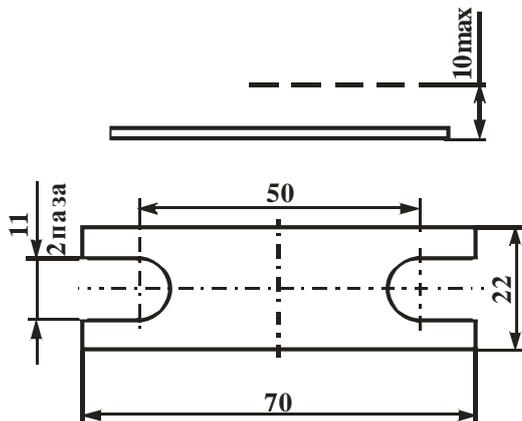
Габаритные и присоединительные размеры Э34-Вх
